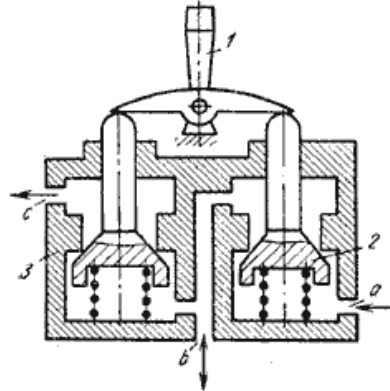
Клапанный гидрораспределитель трехлинейный с качающимся рычагом управления
